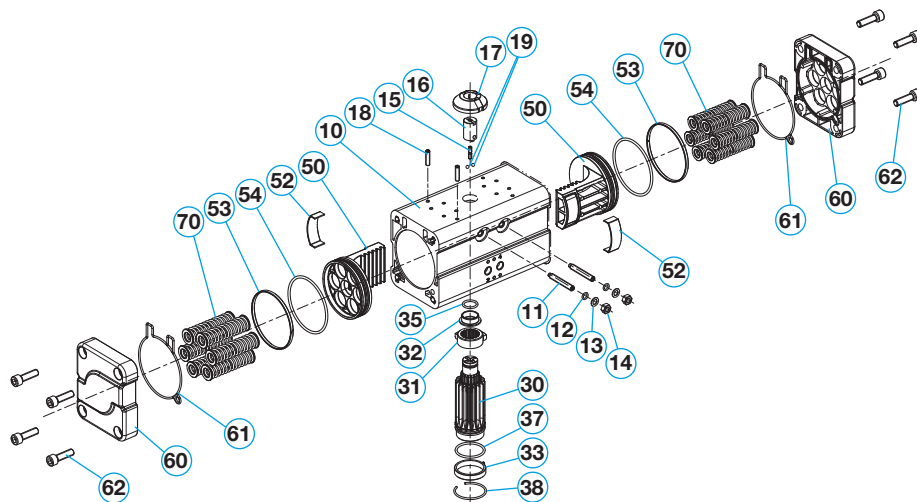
Explosionszeichnung aller Einzelkomponenten Schwenkantrieb actubar
